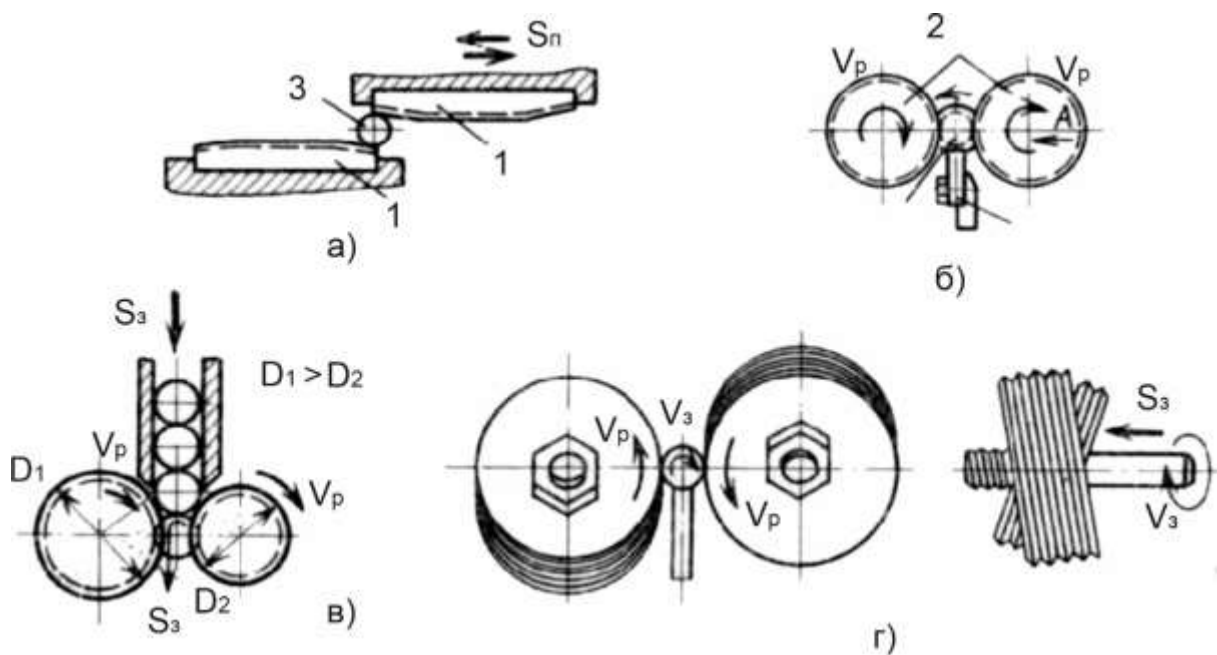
Схема накочування різьблення: а – плоскими плашками; б, в – двома роликками з радіальною подачею; г – двома роликками з тангенційною подачею.
